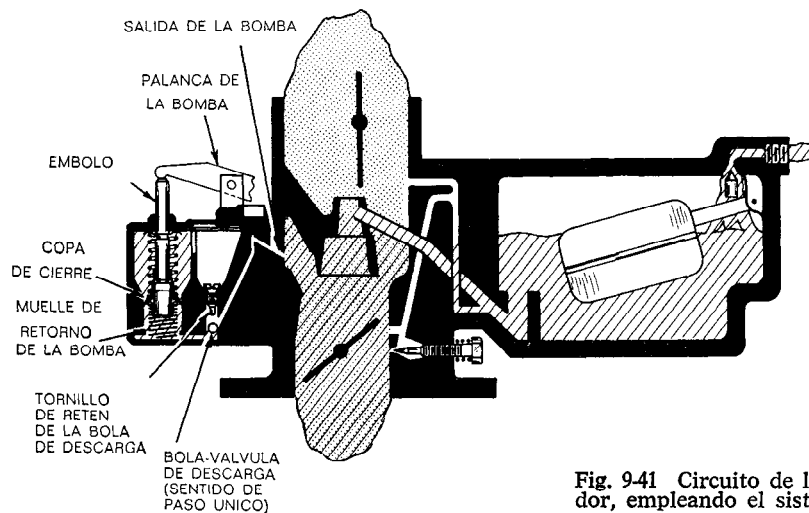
Circuito de la bomba de aceleración en un carburador, empleando el sistema de bomba a émbolo.
